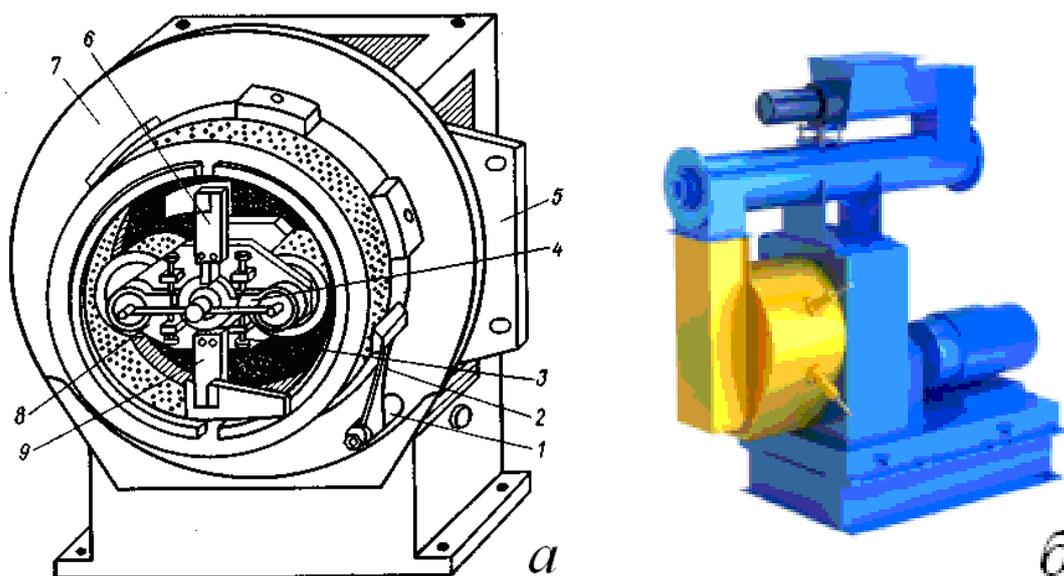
Узел прессования ОГМ-0,8Б (а) и общий вид гранулятора ДГ -1 (б): 1 – ось; 2 – нож; 3 - регулировочный винт; 4 - рычаг; 5 - кронштейн; 6 - короткая лопатка; 7 - щит; 8 - передняя плита; 9 - длинная лопатка
